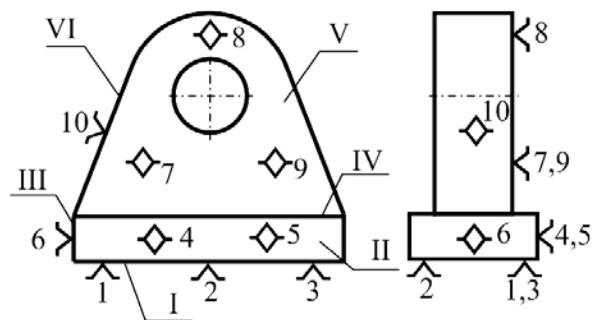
Схема базирования проушины при сборке из двух деталей
